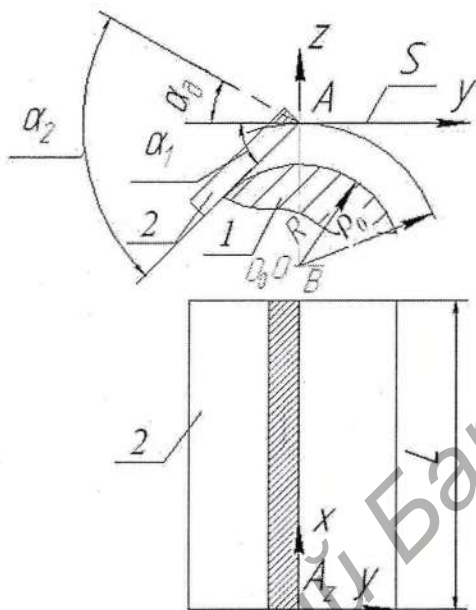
1 – несущий цилиндр; 2 – заготовка ножа
